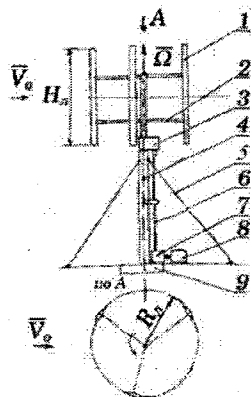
Конструктивная схема вертикально-осевого ветроагрегата:
